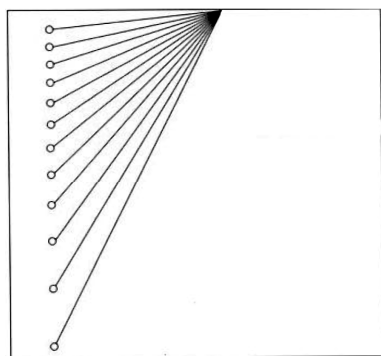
Образец с боковыми цилиндрическими отверстиями
